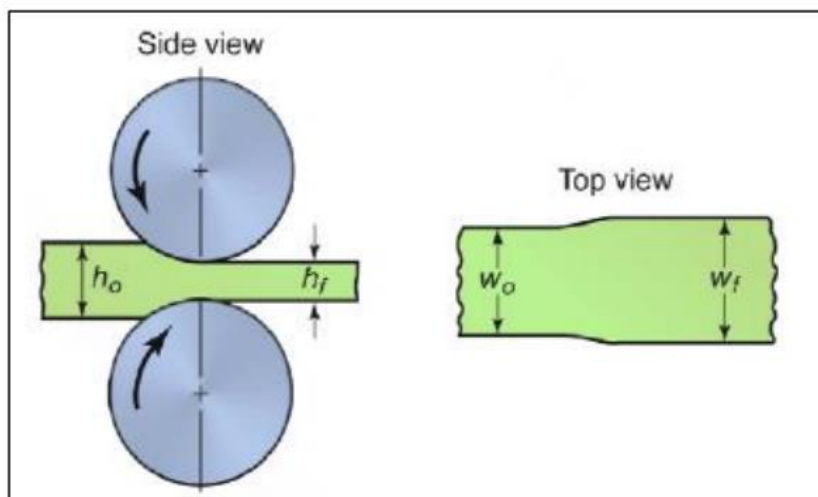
Vista laterale ed in pianta del semilavorato in laminazione, (Di Palma)<sup>92</sup>
